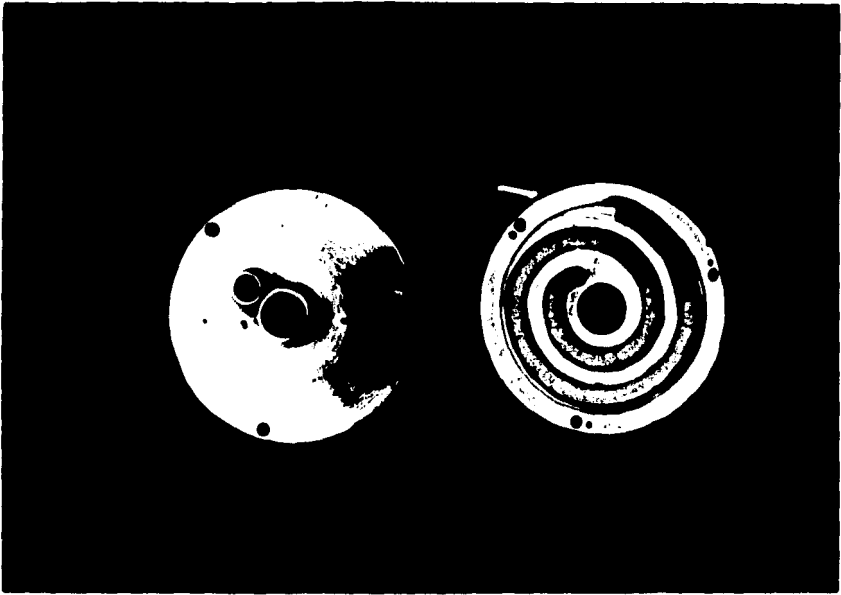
e) Fotografía del intercambiador de enfriamiento sin ensamblar.
